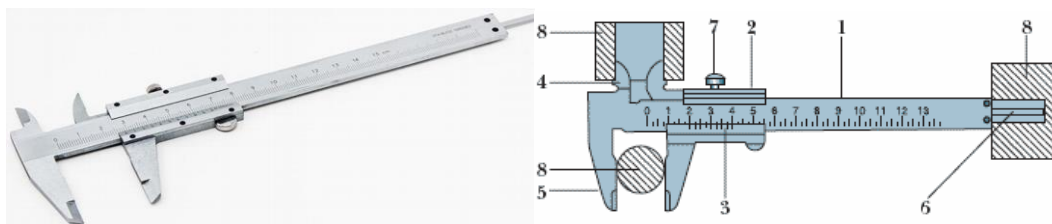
Штангенциркуль: а) загальний вигляд, б) схема приладу.
